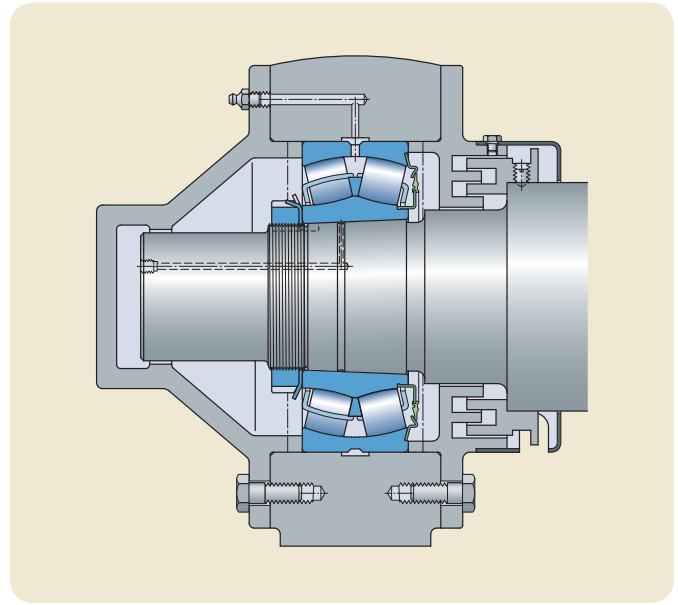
Rodamientos de rodillos a rótula obturados SKF.
